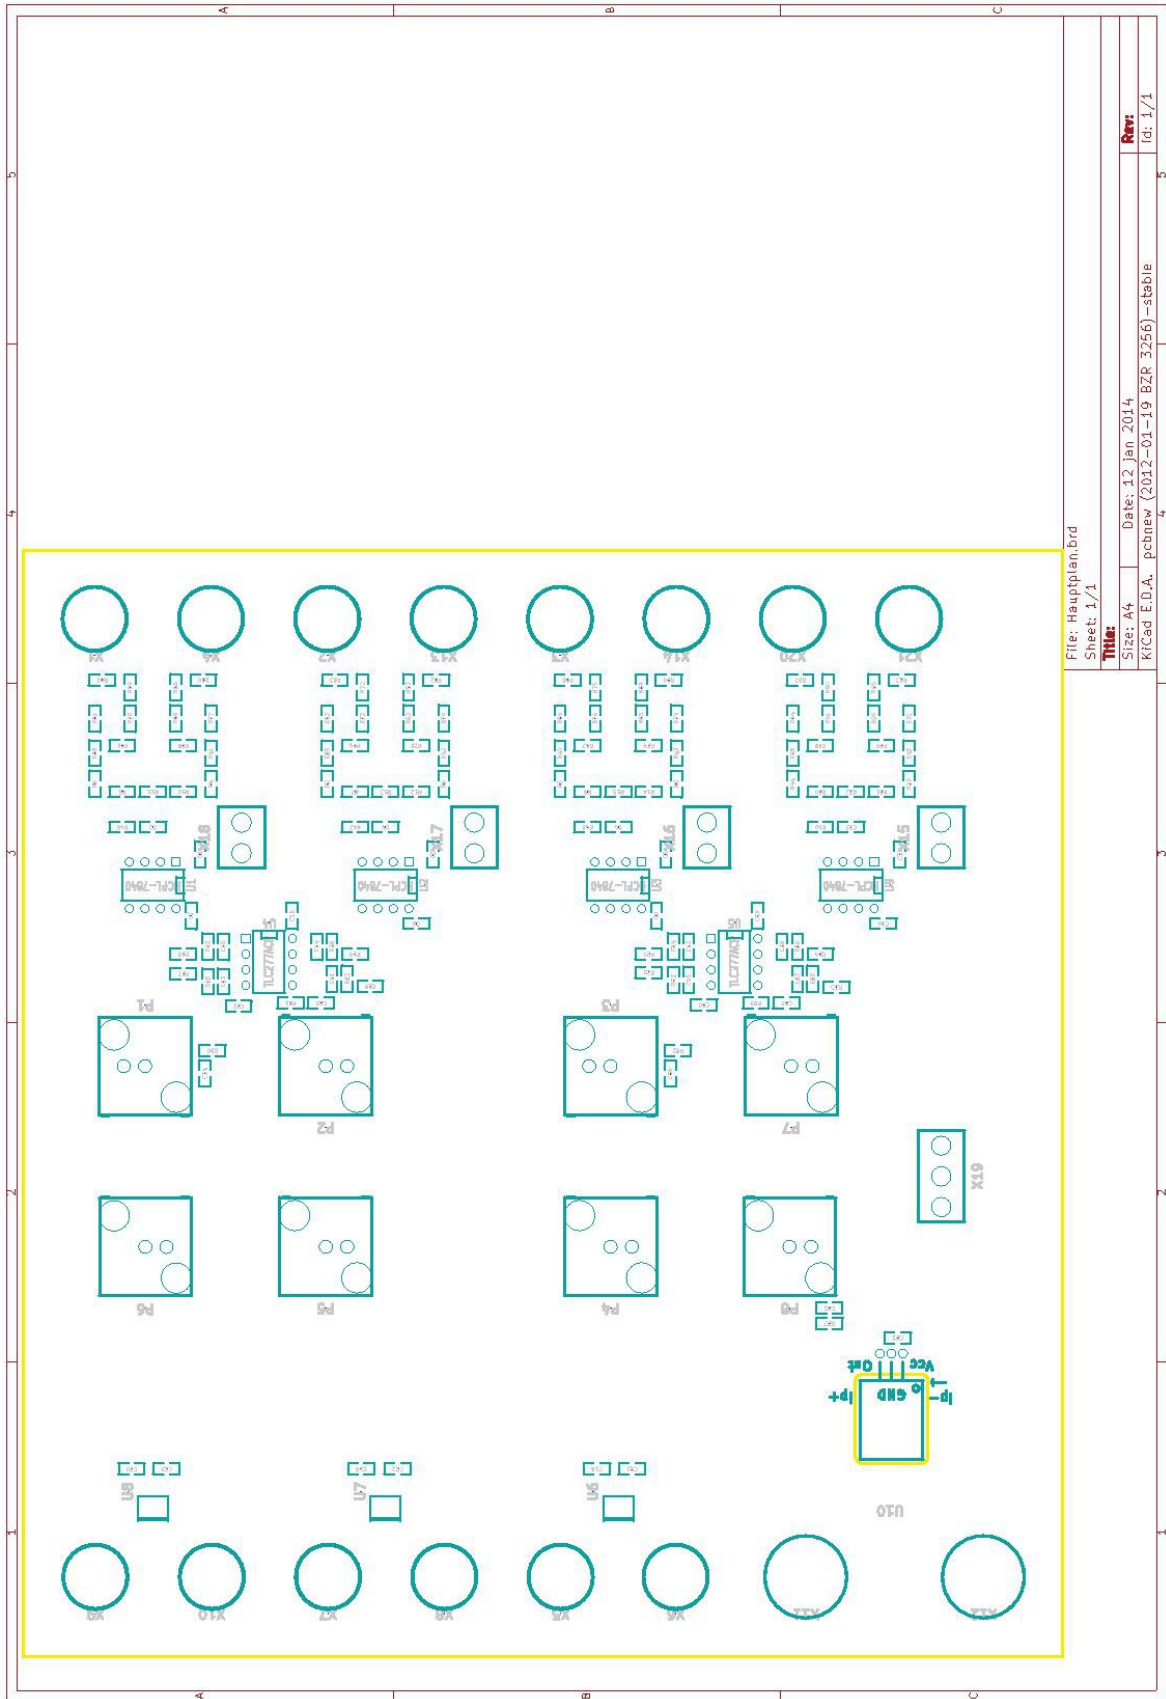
PCB-Layout Siebdruck der Gruppierungen 3 bis 6
